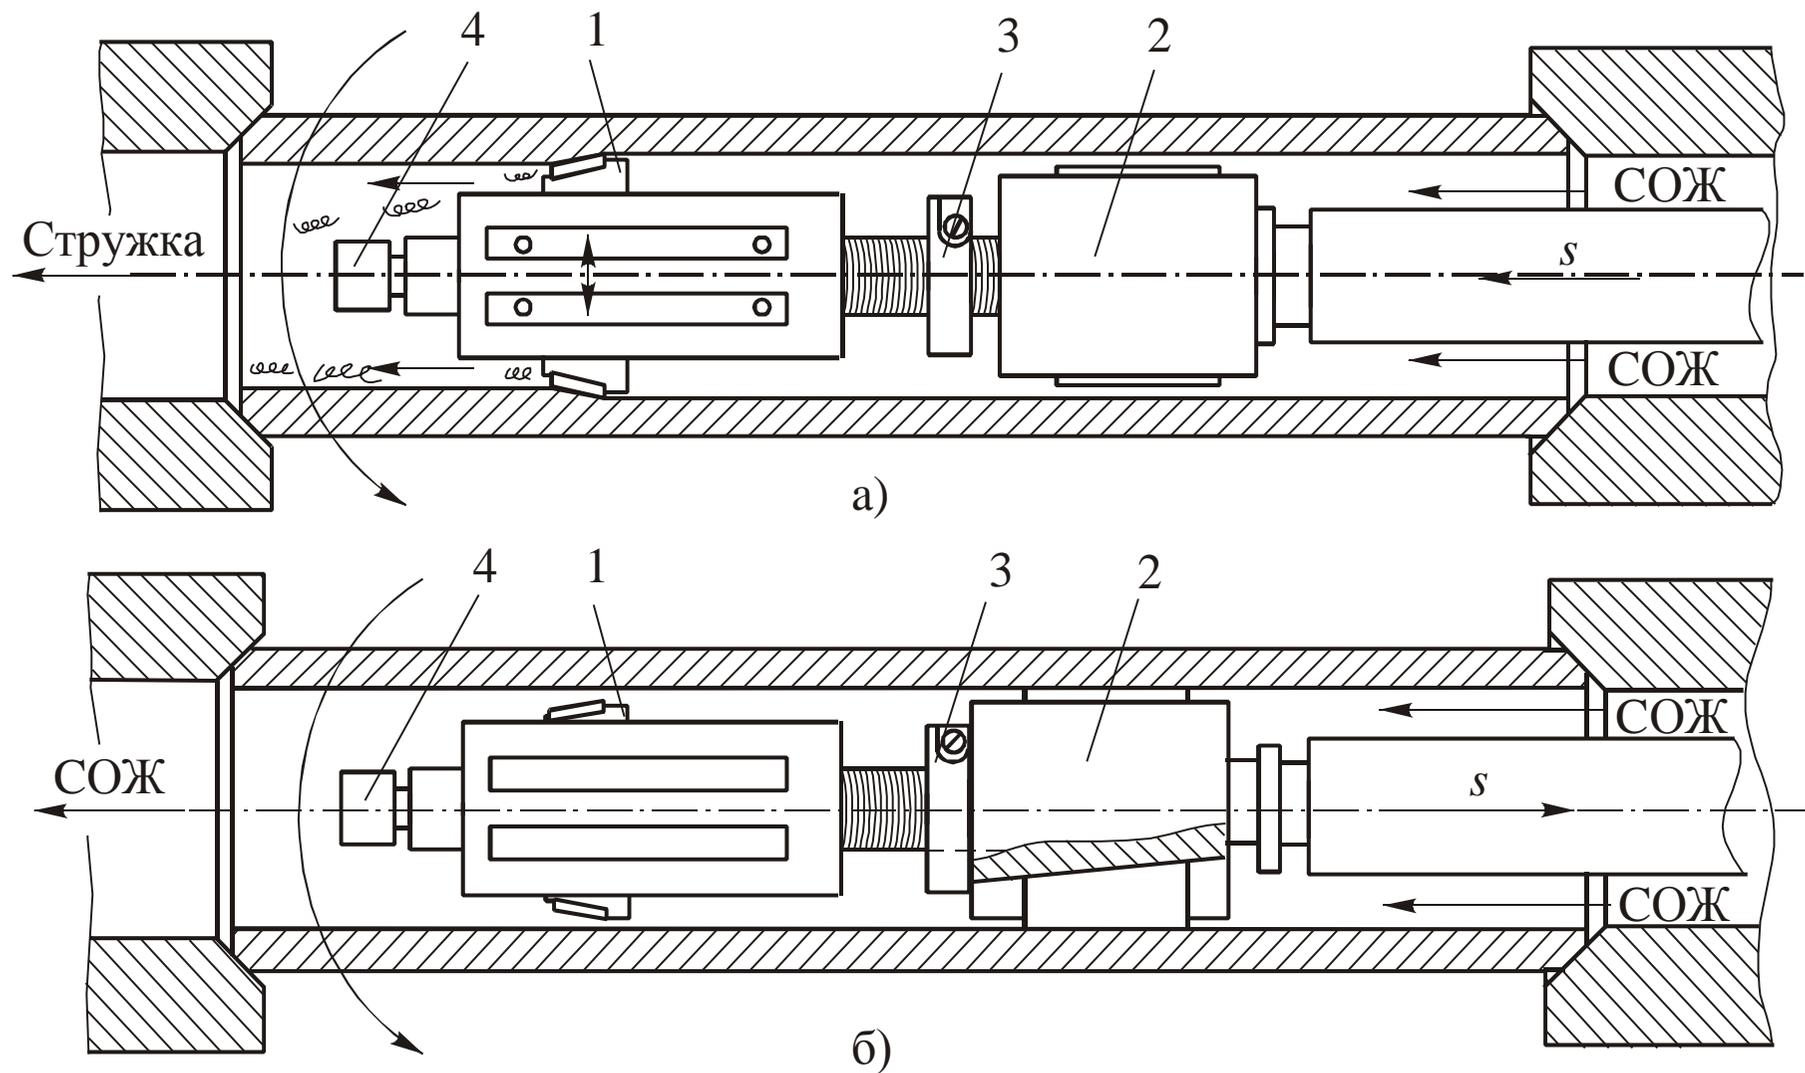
Схемы обработки гильзы гидроцилиндра комбинированным режуще-деформирующим инструментом: 1 – плавающий двухлезвийный расточный блок; 2 – роликовый раскатник; 3 – опорное кольцо; 4 – нажимное устройство
